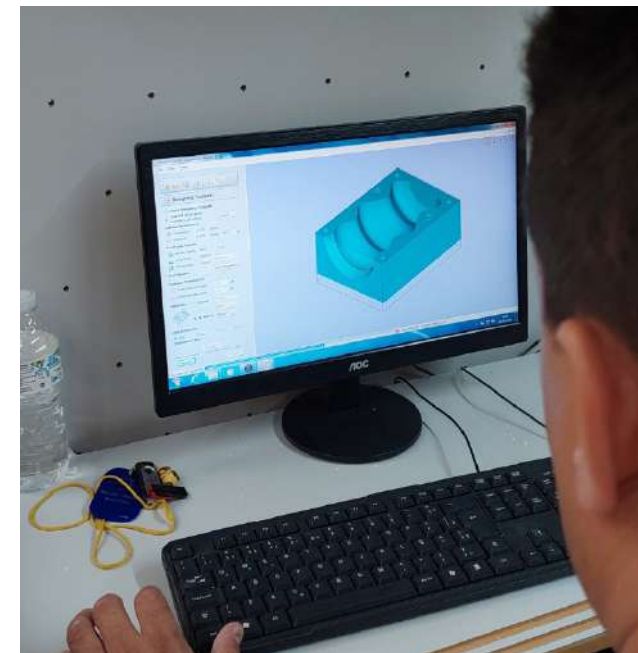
Configuração do arquivo para a usinagem das peças Fonte: a autora.
